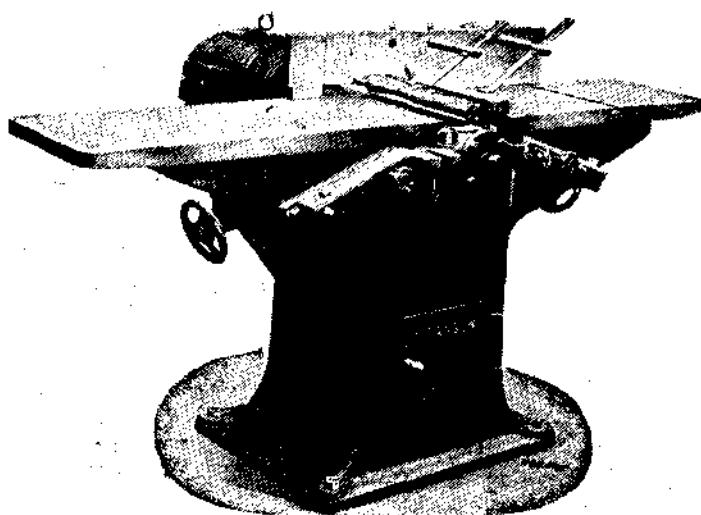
Пригонный, строгальный, фуговочный и калевочный станок.
